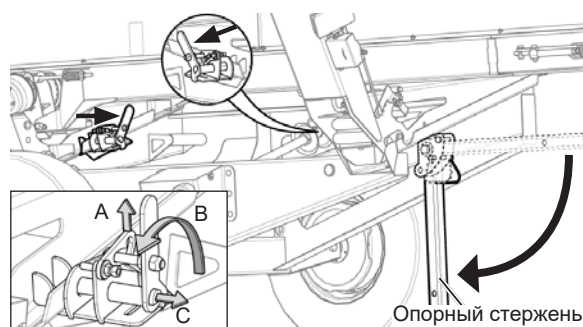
Разблокировка транспортного комплекта и опускание опорного стержня.
